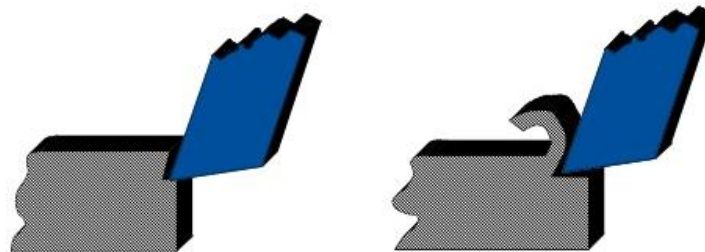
Mecanizado por arranque de viruta mediante herramienta con geometría determinada.
